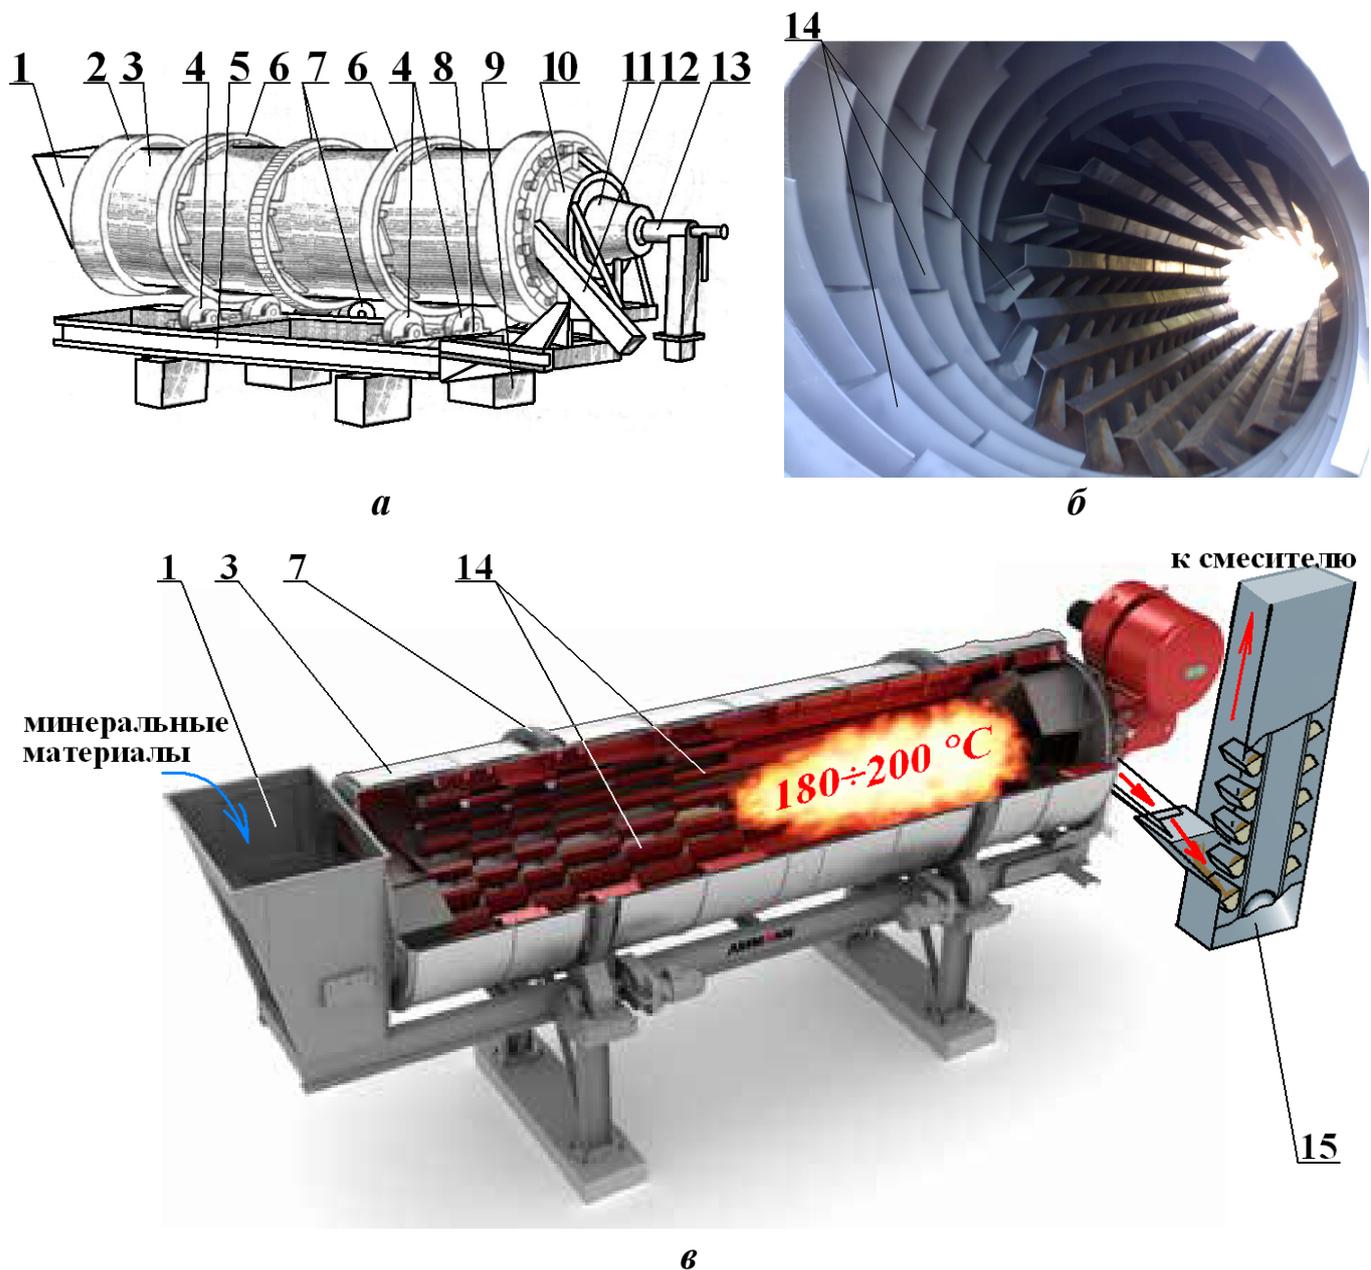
Схема (а), внутренний вид (б) и конструкция (в) сушильного агрегата: 1 – загрузочное устройство; 2 – торцовая обечайка; 3 – сушильный барабан; 4 – опорные ролики; 5 – несущая рама; 6 – бандажи; 7 – зубчатый венец с приводом; 8 – рама опорных роликов; 9 – фундаментные опоры; 10 – топка; 11 – зажигательный конус; 12 – разгрузочное устройство; 13 – форсунка; 14 – направляющие и ковшеобразные лопасти; 15 – горячий элеватор
